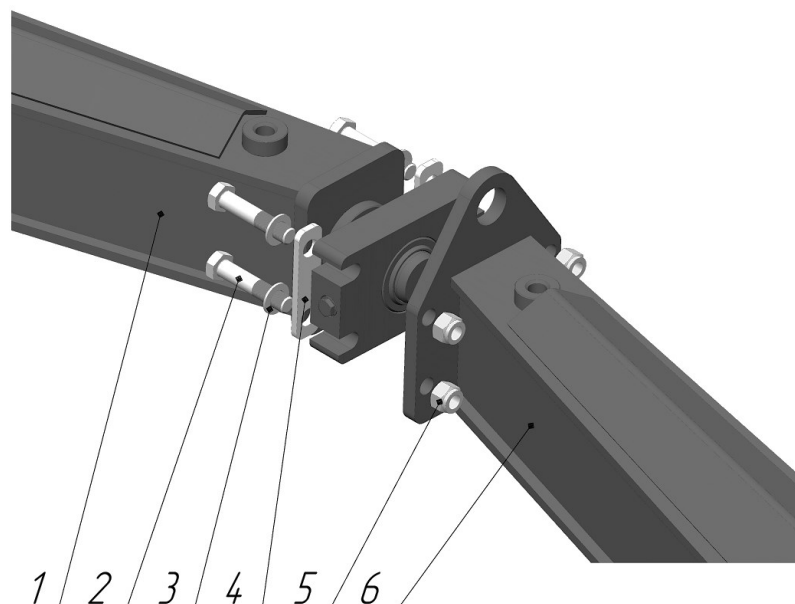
Стыковка правой и левой половин толкающего бруса
